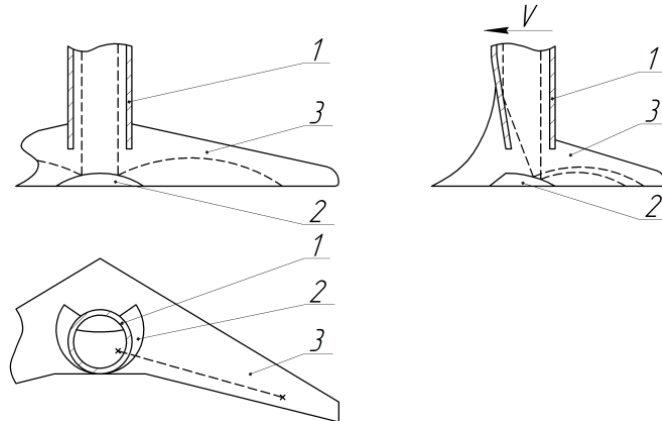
Схема сошника для внутрипочвенного разбросного посева:
